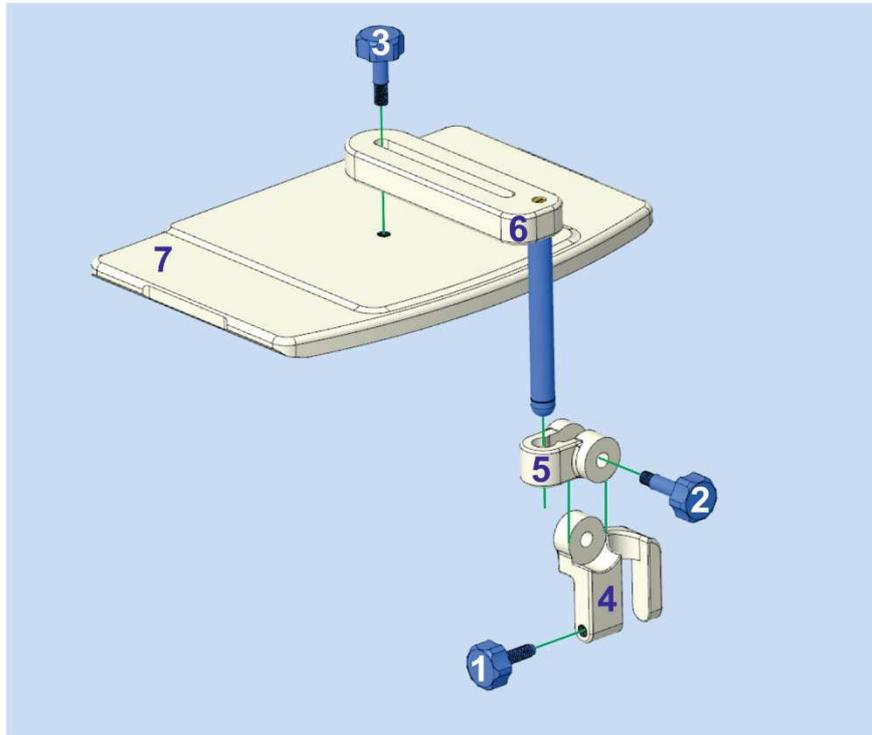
Montaje del soporte de la bobina ER en configuración "HLD Bobina".
